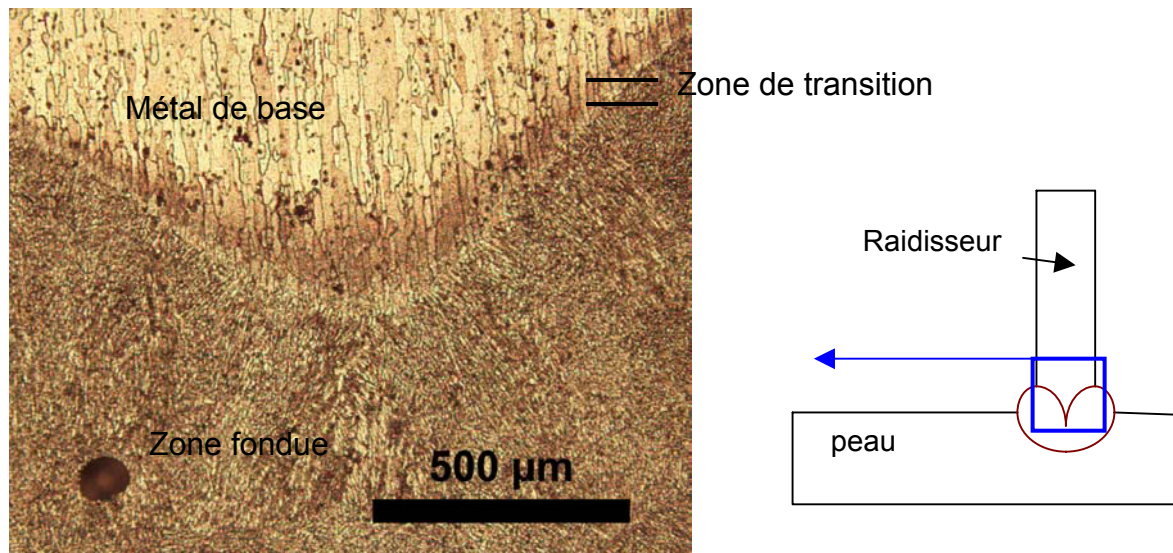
Vue d'une soudure en T après attaque chimique
